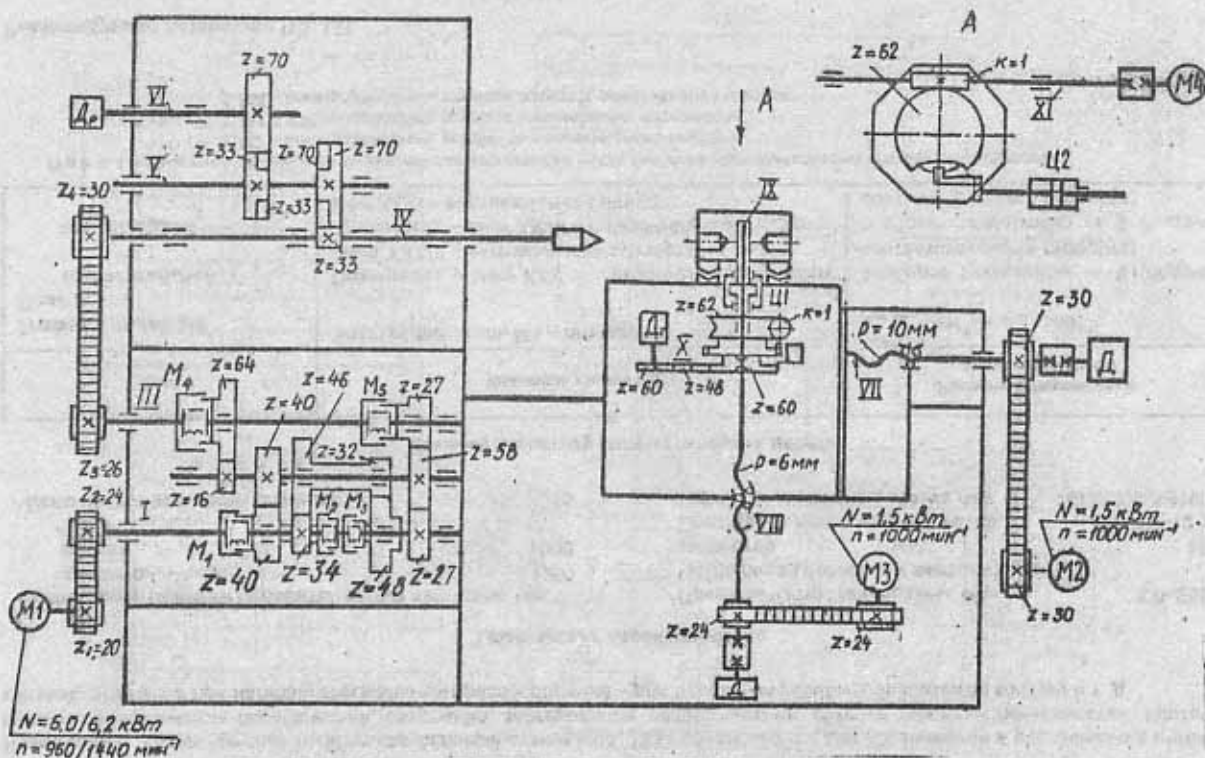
Кинематическая схема токарно-револьверного станка мод. 1В340ФЗ с ЧПУ
